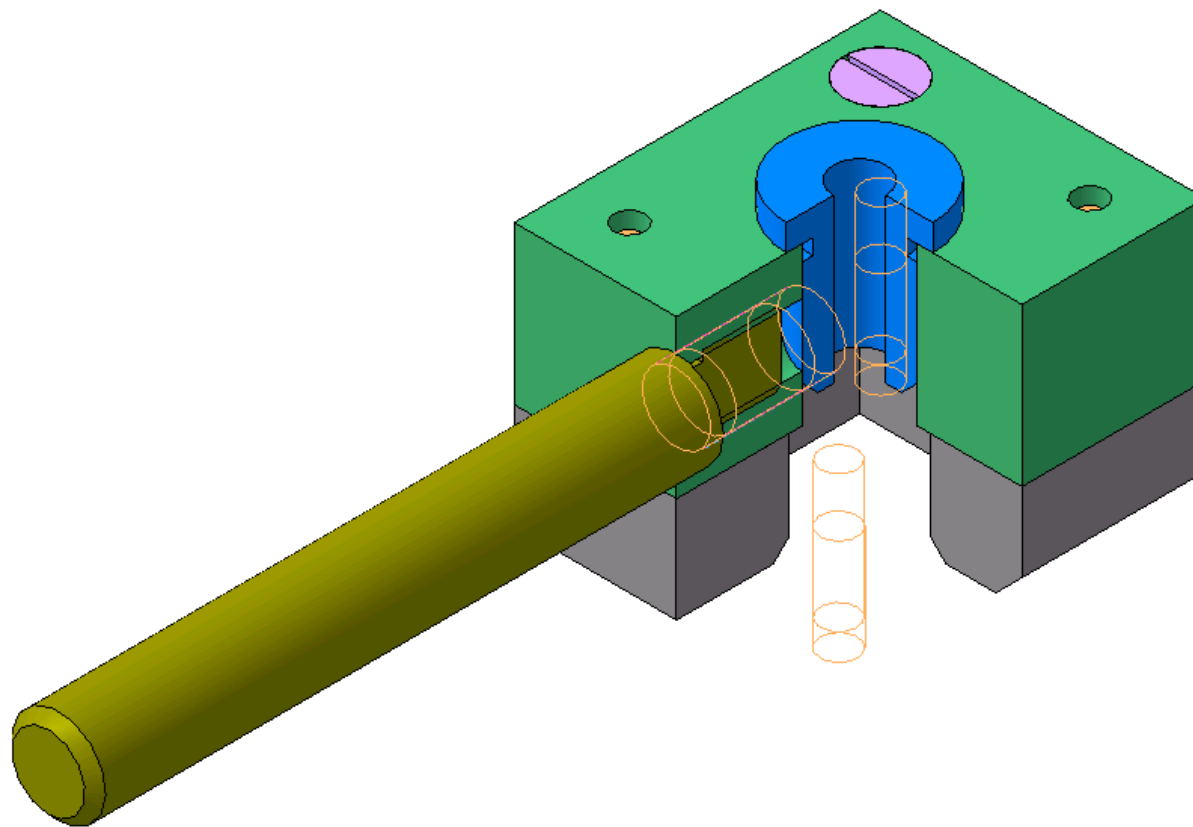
3D-модель сборки изделия «Кондуктор-2» (варианты 5, 25)
